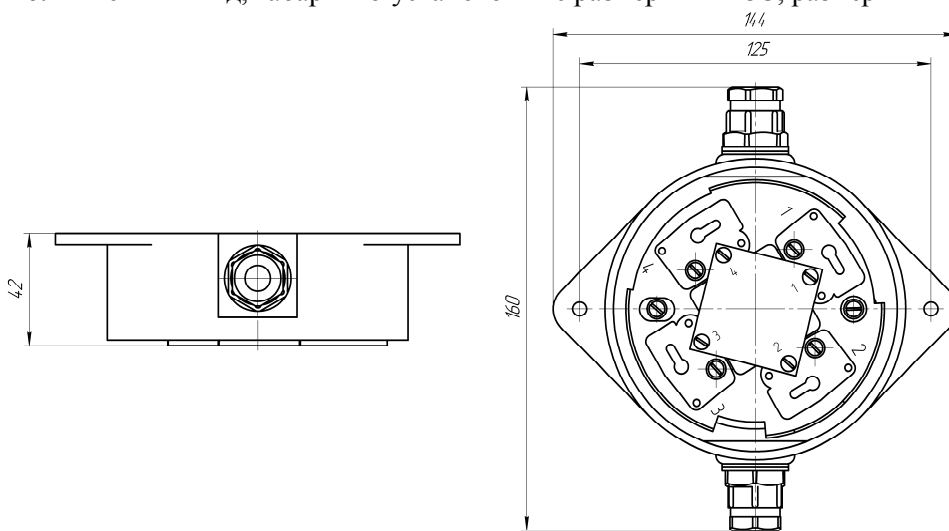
Внешний вид, габаритно-установочные размеры МКЗС-01, размеры в мм.
